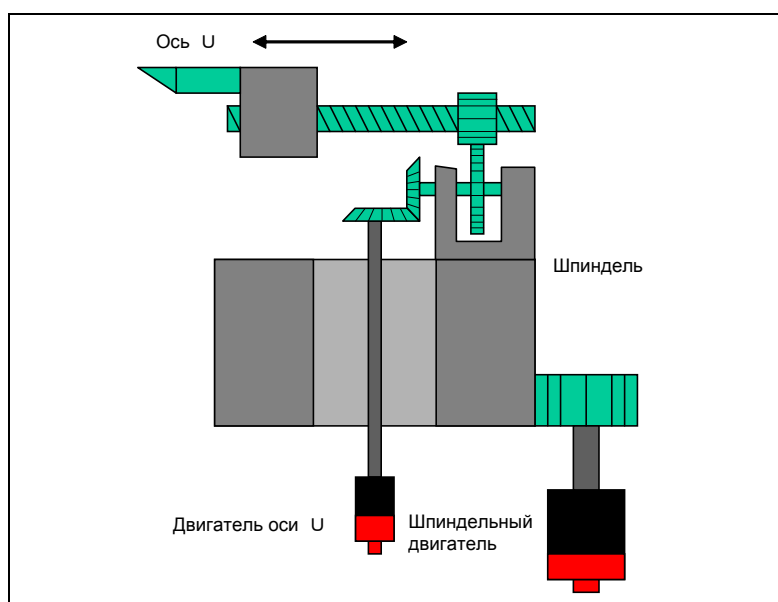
(b) Пример конструкции станка с осью U
